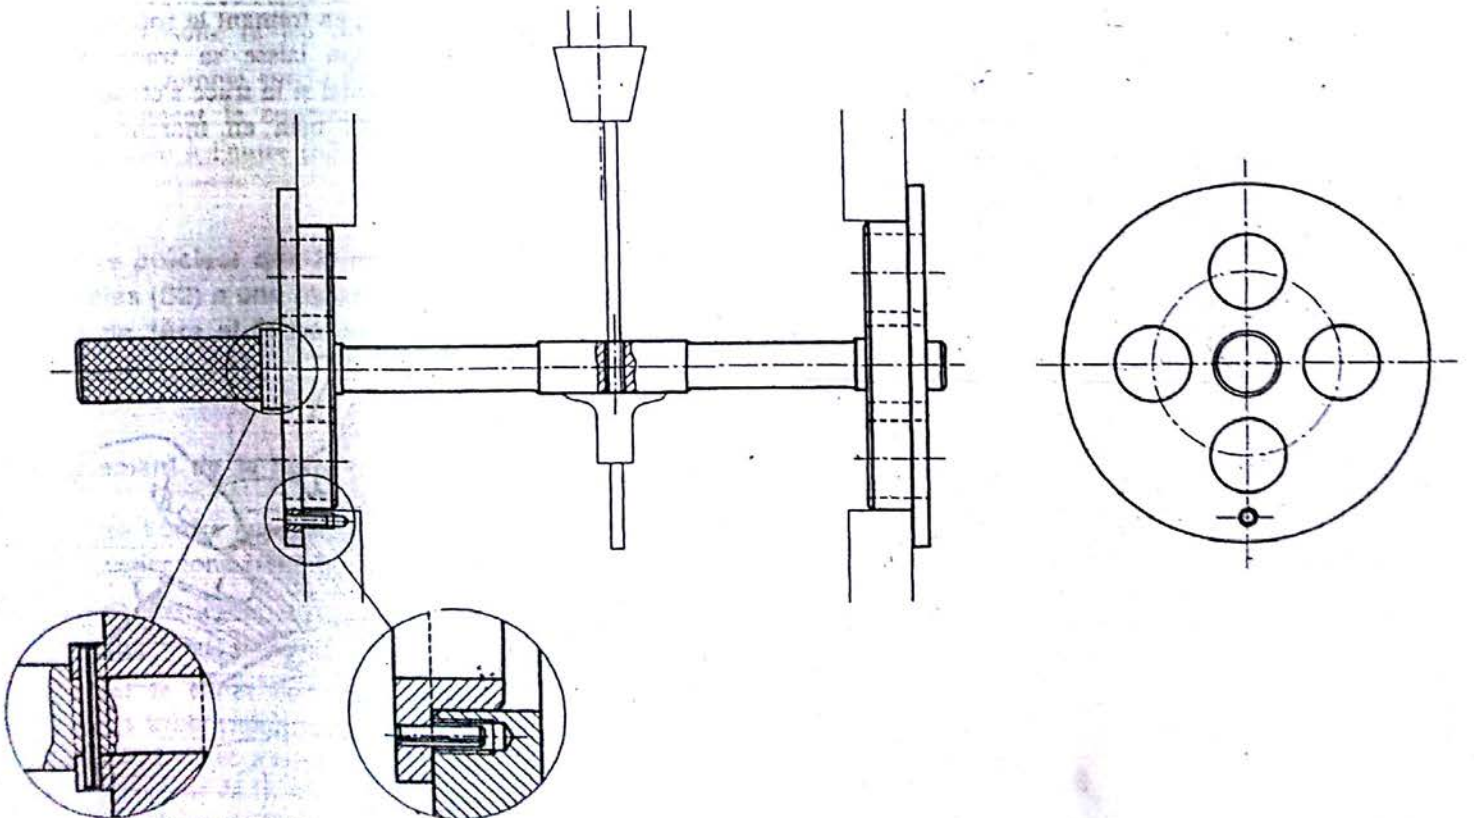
/16. - Outil de contrôle de la position du pignon à queue - Réf. 21 205 SO.
